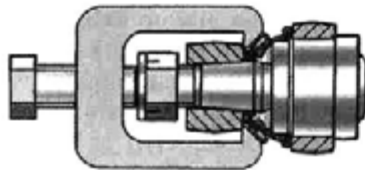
Выпрессовка пальца шарнира рулевых тяг универсальным съемником
